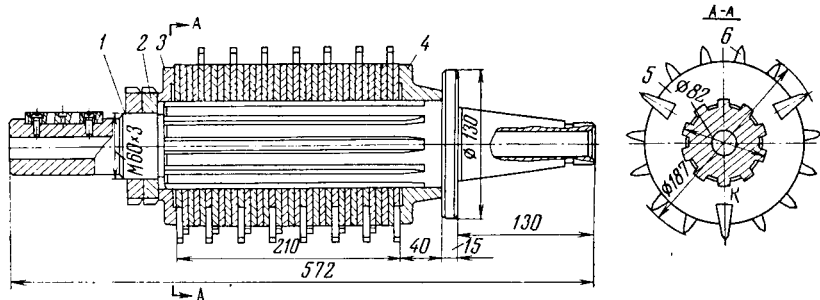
Наколочный барабан станка ПКБ ЦП МПС
